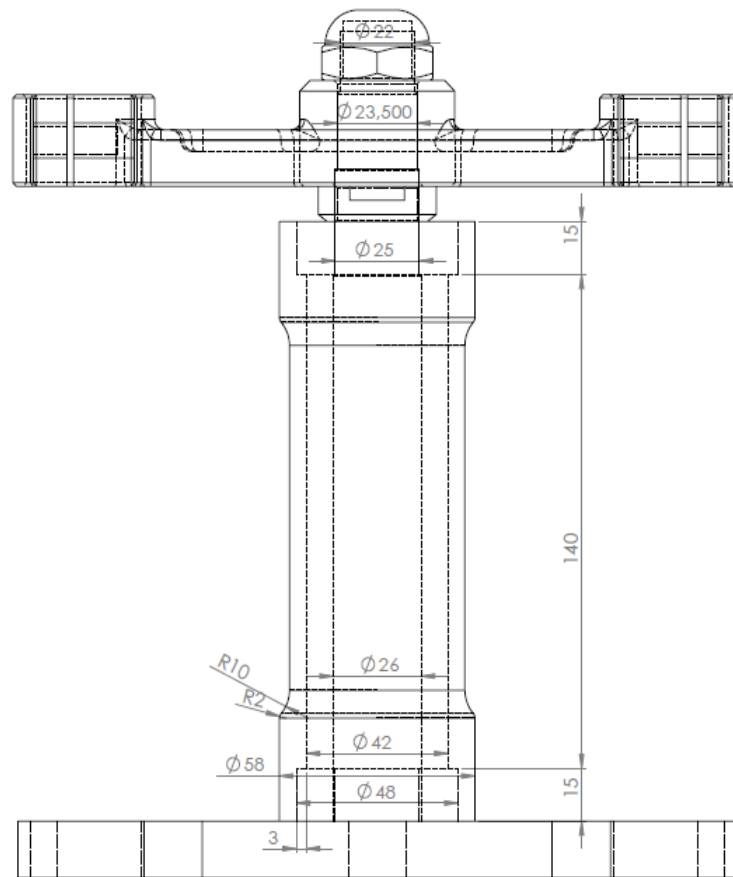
Plano y diseño de la columna de dirección de fabricación propia
